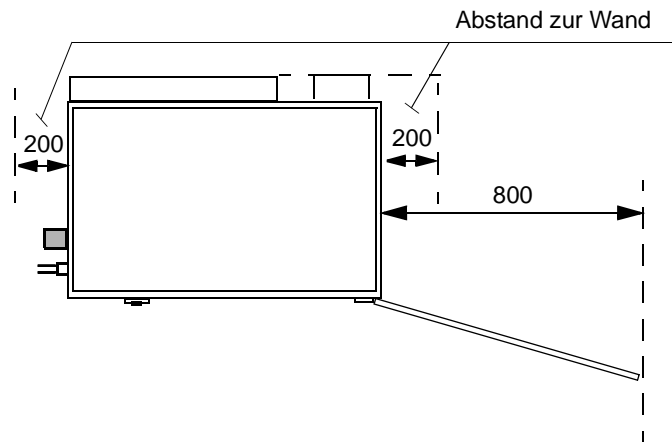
Draufsicht des Manipulators (Abmessungen in mm)
